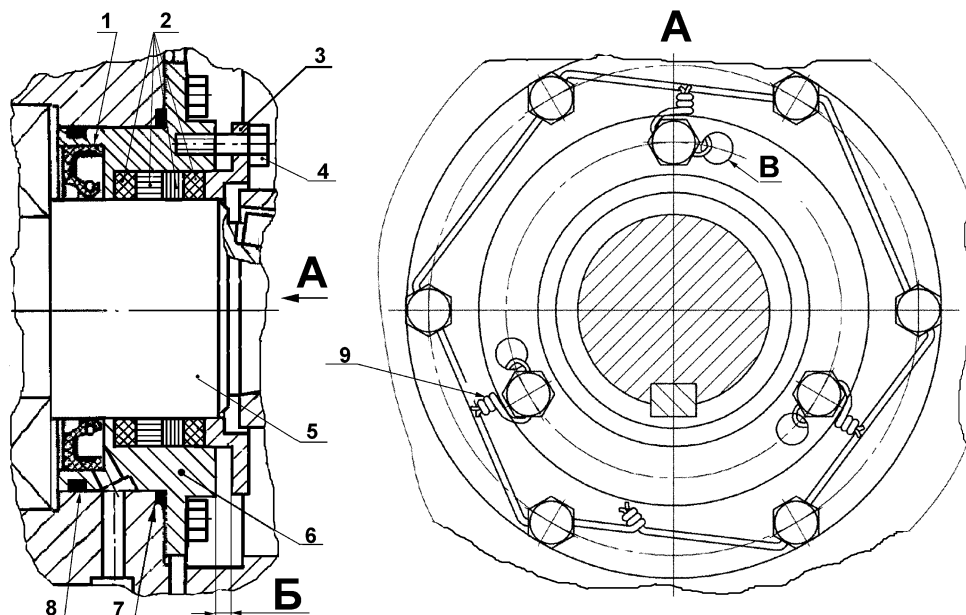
Уплотнение вала ступени нормального давления: 1 — манжета; 2 — кольцо уплотнительное из набивки; 3 — кольцо нажимное; 4 — болт; 5 — вал; 6 — стакан; 9 — проволока контрольная; 7; 8 — кольца уплотнительные.
